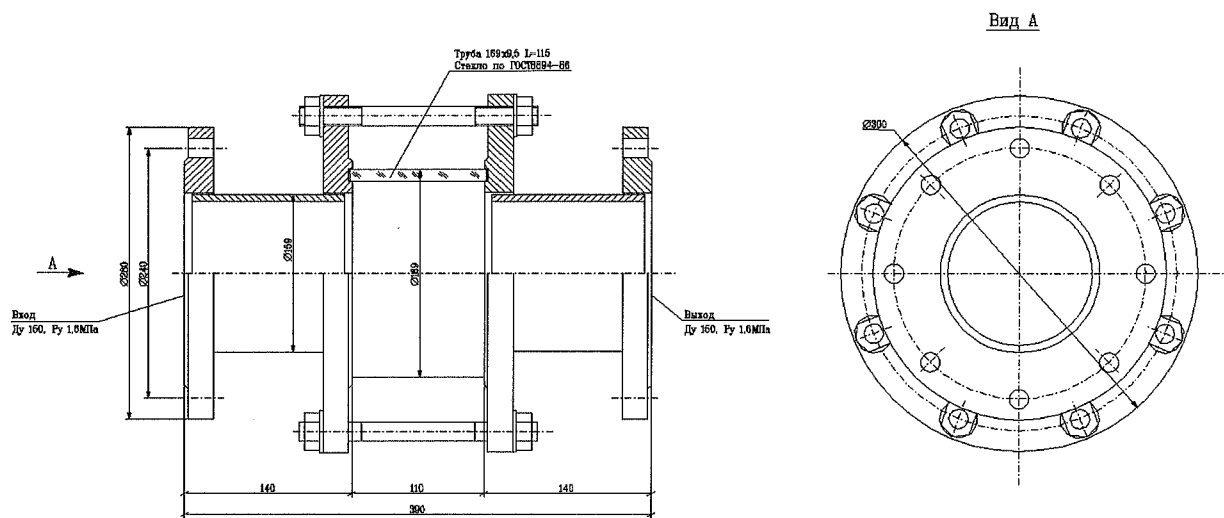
Габаритный чертеж фонаря смотрового LDF11-15AX001, LDF21-25AX001
